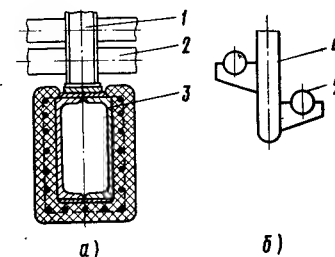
Конструкция перегревателя в соединительном газоходе:
